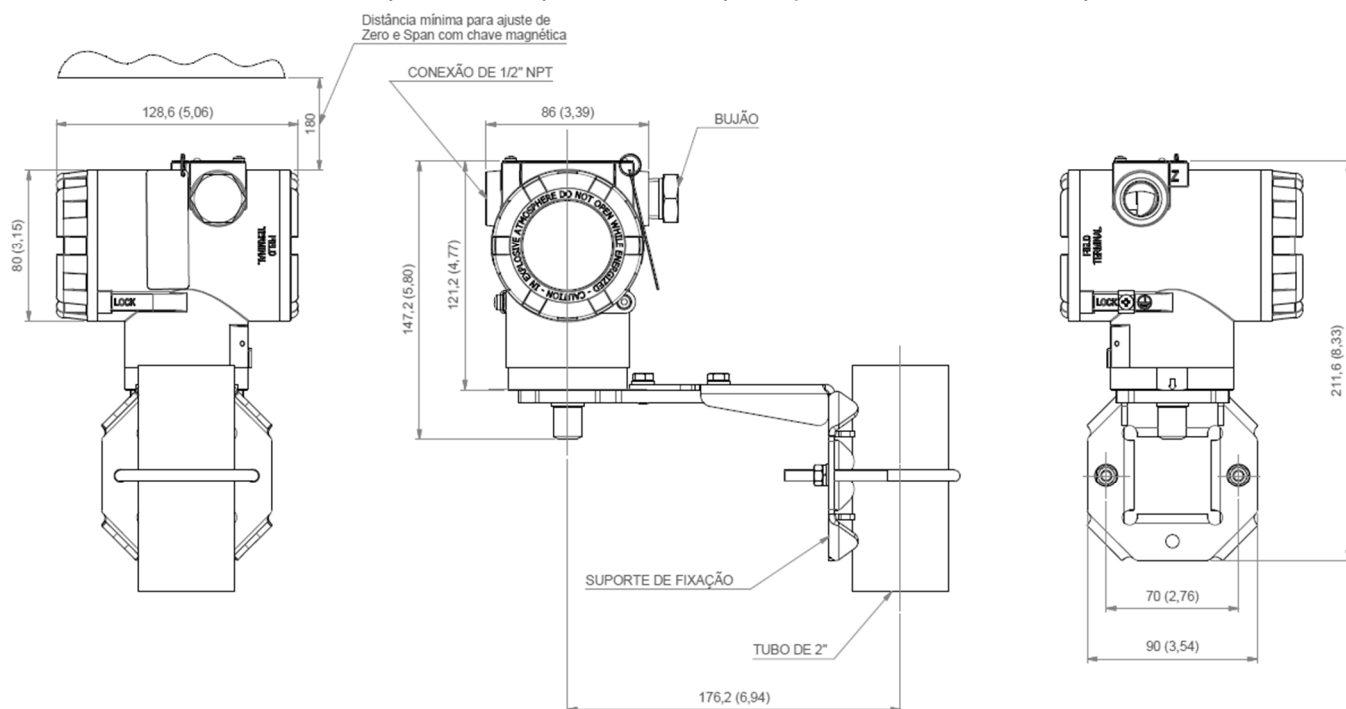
Desenho dimensional e esquema de montagem do VTP10-P.
